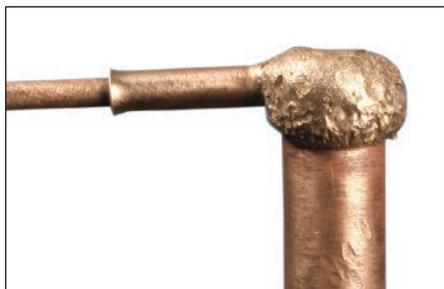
Está listo para realizar otra conexión Cadweld.
